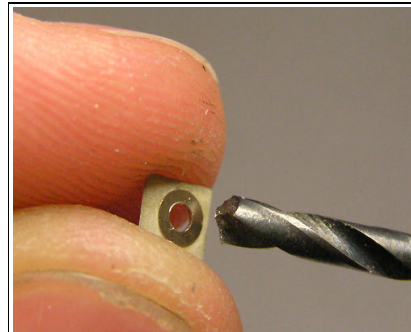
Das Loch beidseitig mit dem Bohrer entgraten.
